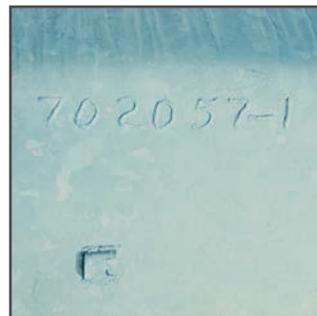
Des cordons de soudure peuvent être utilisés pour identifier la pièce fabriquée
